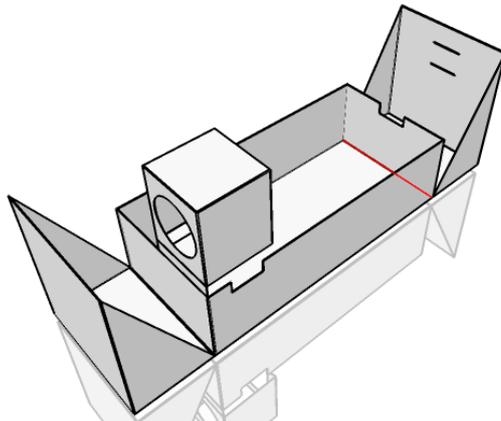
Guía de plegado. Plegado base realizado. Fuente: Elaboración propia.
